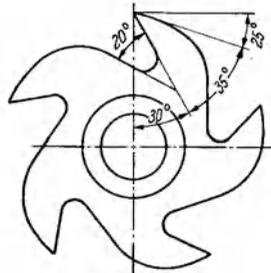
Schnittwinkel am hinterdrehten Fräser.
